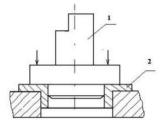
Схема установки заготовки 1 наружной цилиндрической и плоской торцевой поверхностью во втулку 2.
